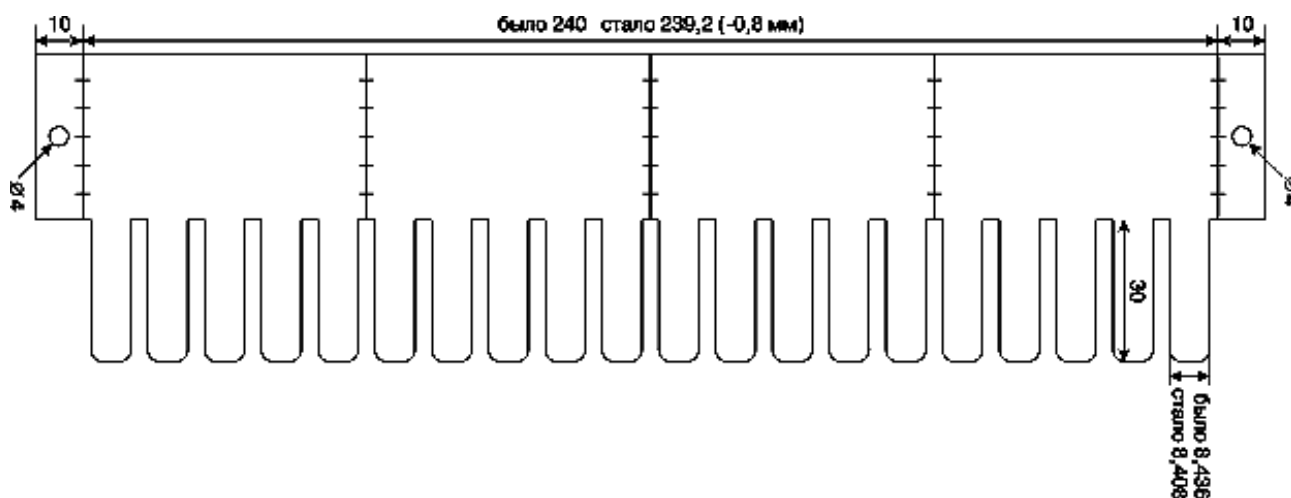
Шаблон штанцевальной формы для вырубки заготовок матриц типографским прессом. Приведены допуски, компенсирующие увеличение размеров гребенки при вырубке
